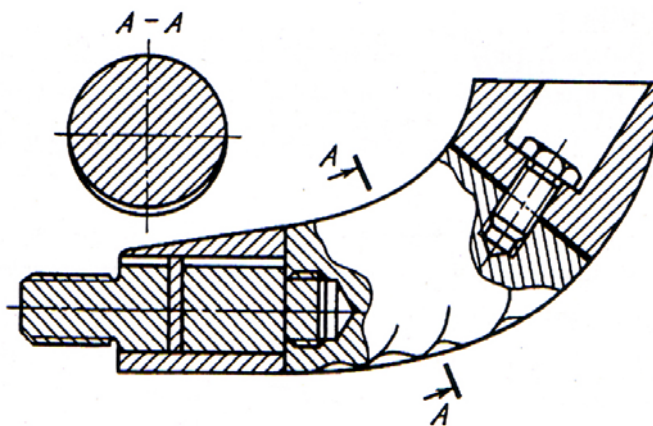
Сборно-разборная конструкция рогообразного сердечника
